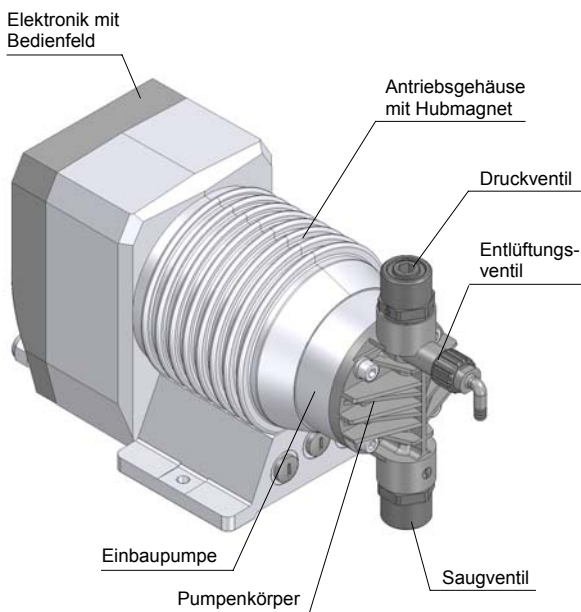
(Baugruppen der Magnet-Membranpumpe)
